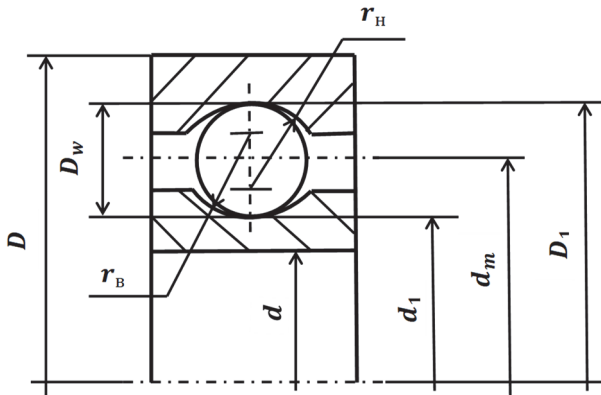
Основные размеры поверхностей качения шарикового радиального подшипника
